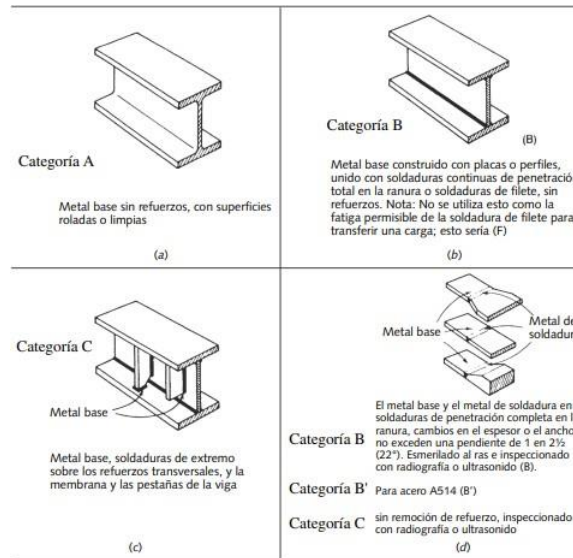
Algunas categorías de ensambles soldados [28].
